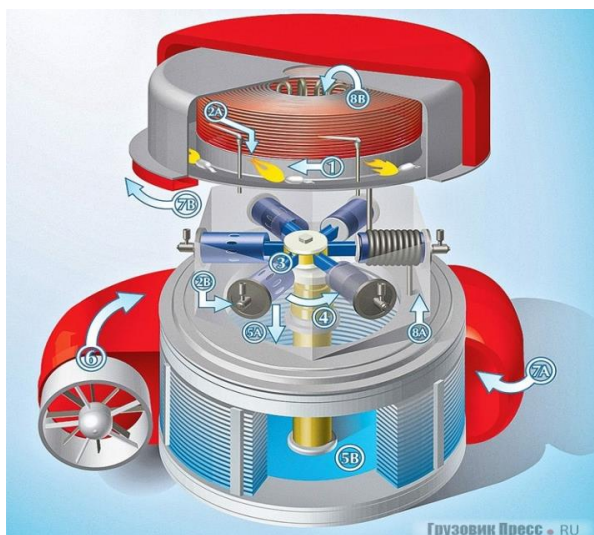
Паровой многотопливный двигатель Waste Head Engine
